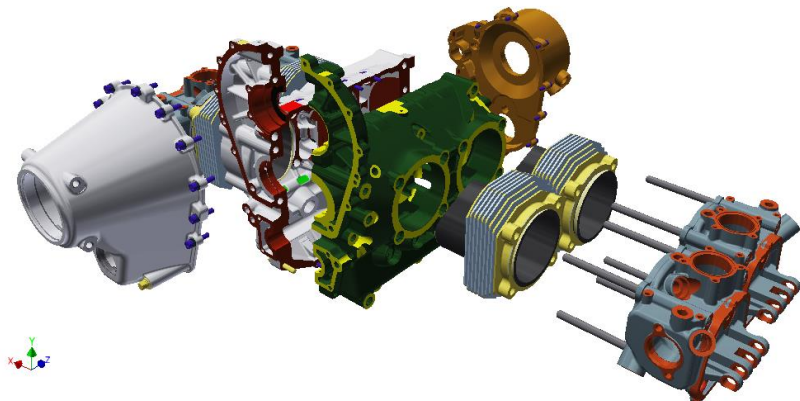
Корпусные детали двигателя в разведенном состоянии
